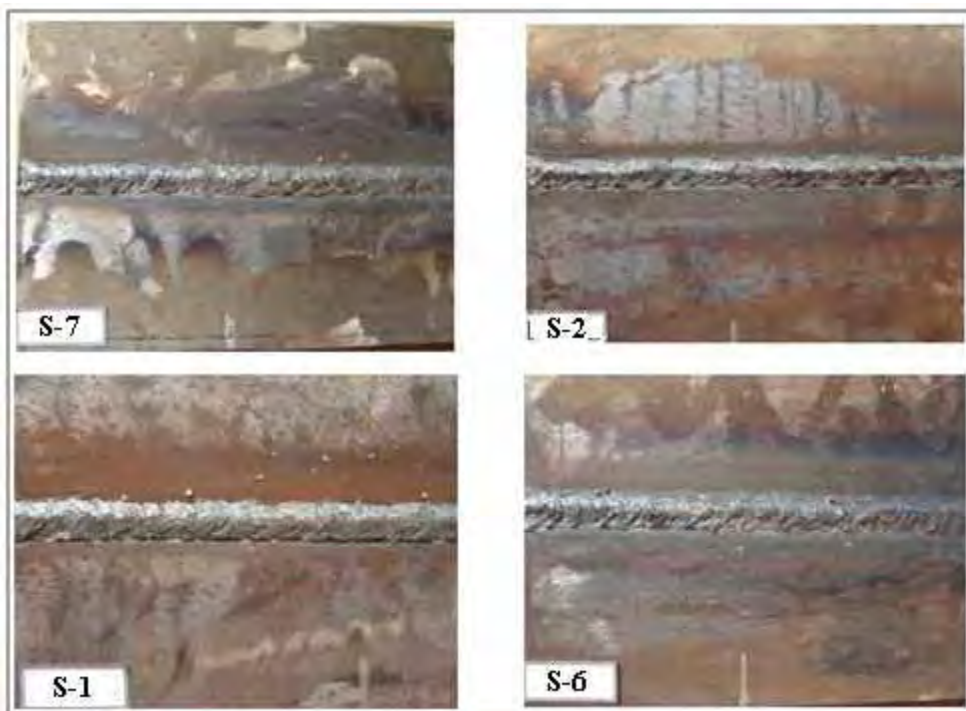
Detalhe visual dos 2ºs cordões das juntas soldadas.
